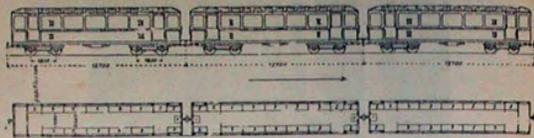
Ferrovia elevata e sotterranea di Berlino. Vista e pianta delle vetture.
